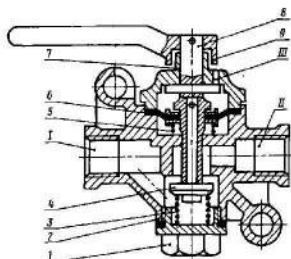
Кран разобщительный: 1 — пробка; 2 — корпус; 3 — пружина клапана; 4 — клапан; 5 — пружина штока; 6 — шток с диафрагмой; 7 — крышка; 8 — толкатель; 9 — рукоятка; I, II — выходы
